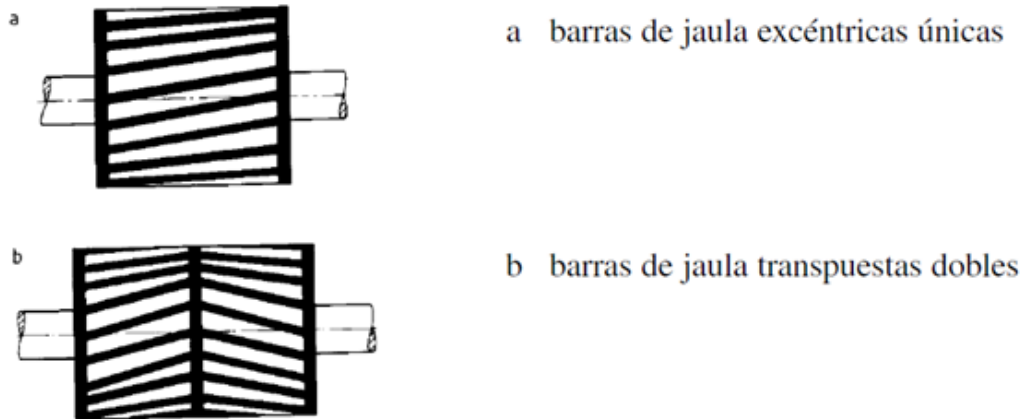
Tipos de bobinado del motor jaula de ardilla
